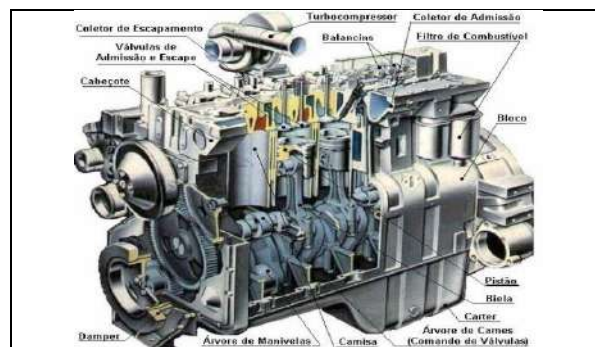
Demonstrativo de Motor a Diesel com partes vista em corte com a descrição.
